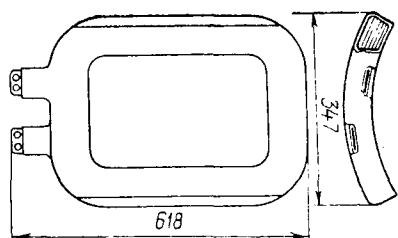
Катушка главного полюса двигателя НВ-418К6
